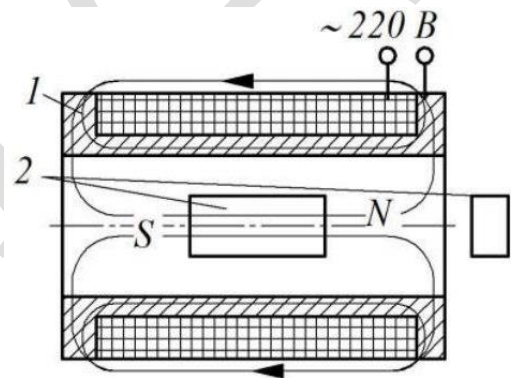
Обробка постійним магнітним полем: 1 – соленоїд; 2 – заготовка [27]
